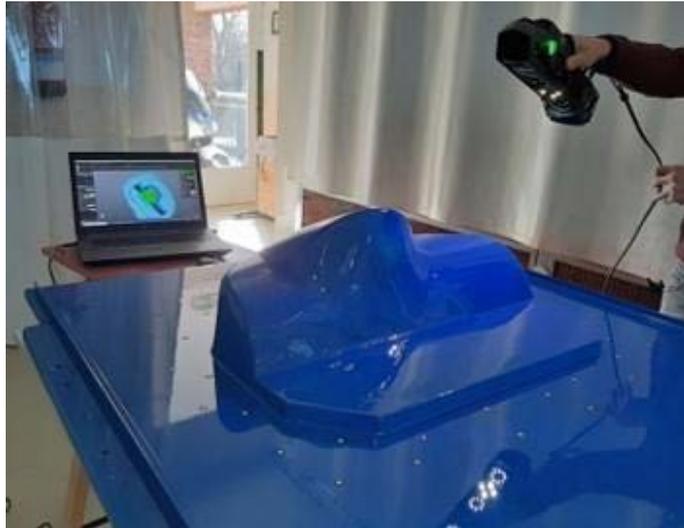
Werkzeug für Kohlefaserteil mit Creaform Go!Scan Spark scannen. Quelle: Tknika
